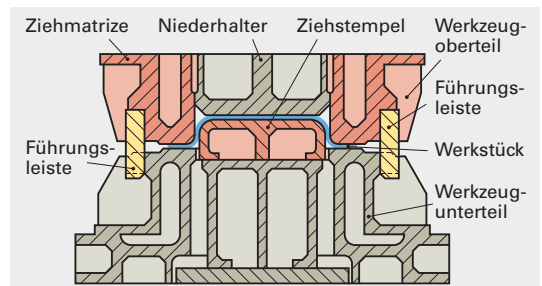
Mehrfachwirkendes Ziehwerkzeug
